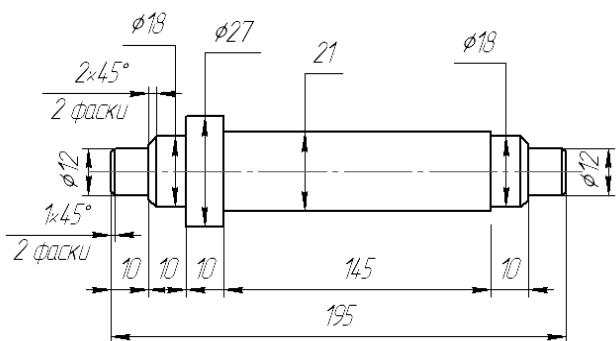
Оправка для выпрессовки и запрессовки гнезда перепускного клапана.
